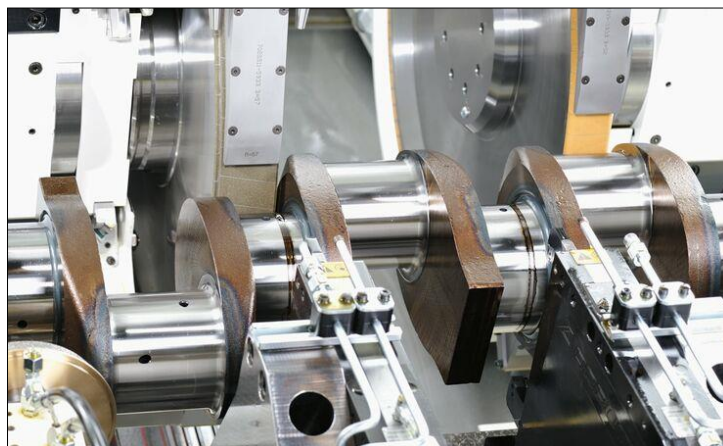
Шліфування колінчастого вала на верстаті фірми Junker [11]
